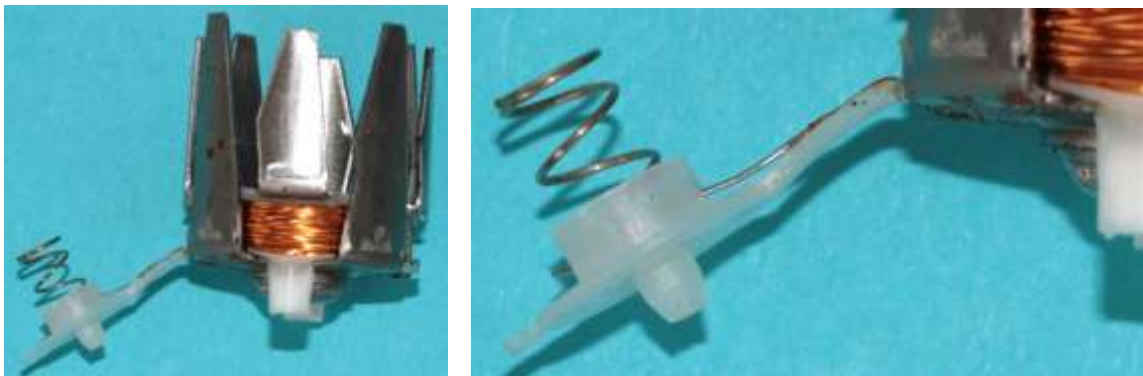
Ausleger für die Befestigung der Spannung führenden Schraubenfeder
